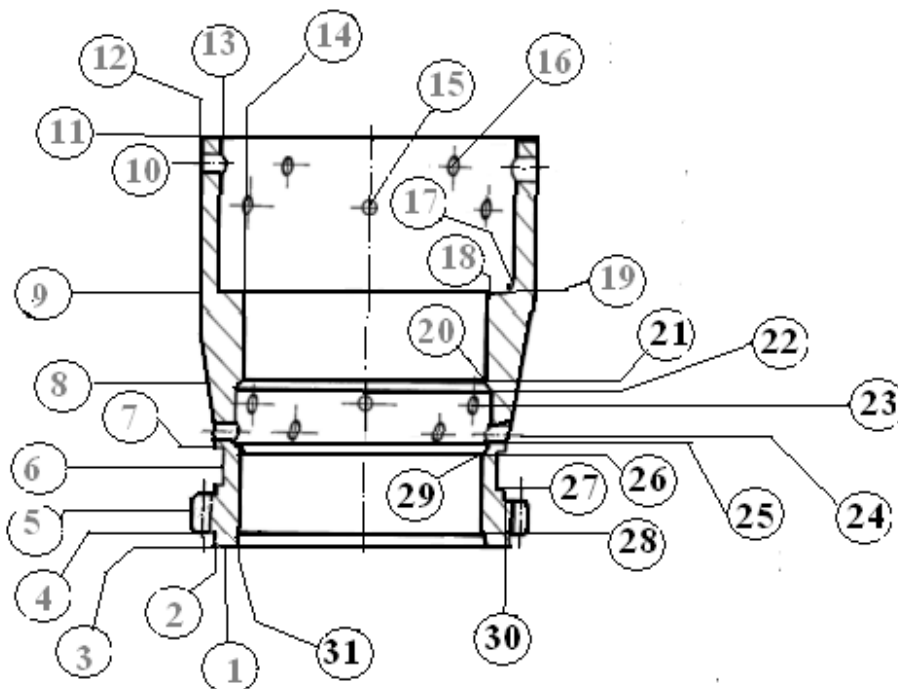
Ескіз деталі «Шестерня» з визначеними поверхнями
